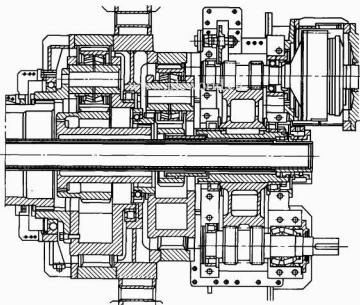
两级行星和一级圆柱齿轮分流传动齿轮箱的结构
